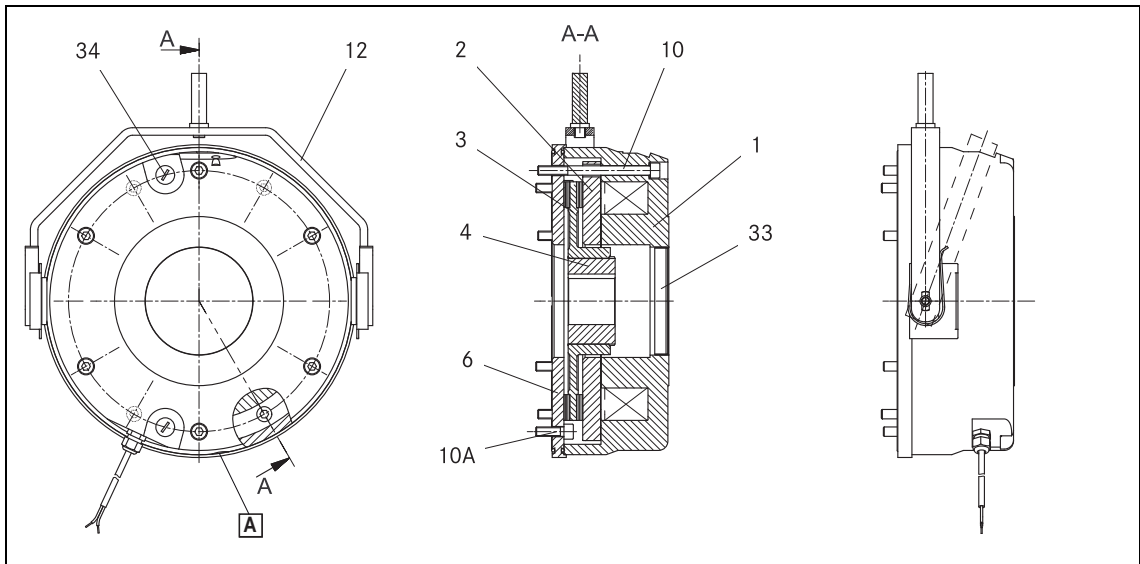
Aufbau der Federkraftbremse BFK471-25, Ausführung mit einem Rotor
